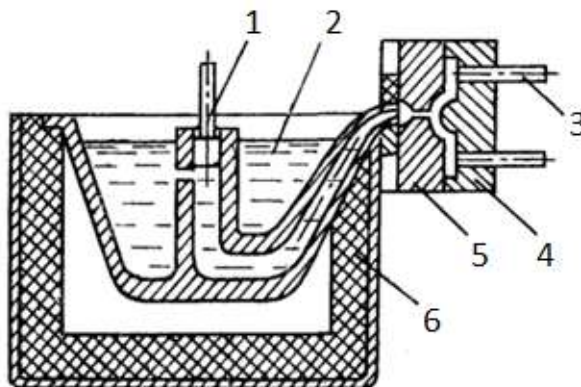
Схема машини для лиття під ВТ з гарячою камерою стискання: 1 – стискувальний поршень; 2 – рідкий метал; 3 – виштовхувачі; 4, 5 – частини форми; 6 – корпус з електронагрівачем
